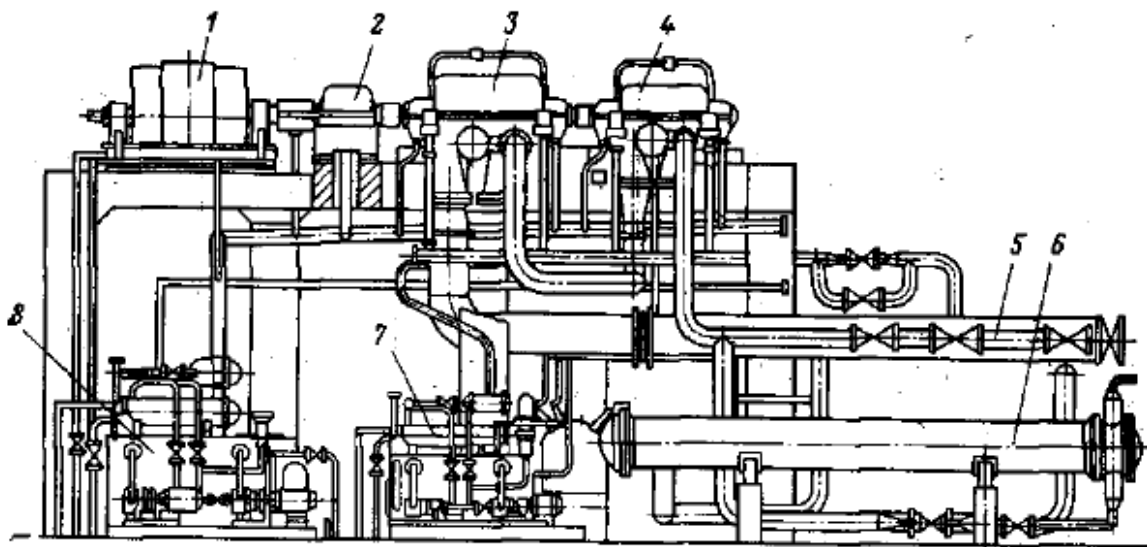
Центробежный компрессор 43ЦКО-160/15:
